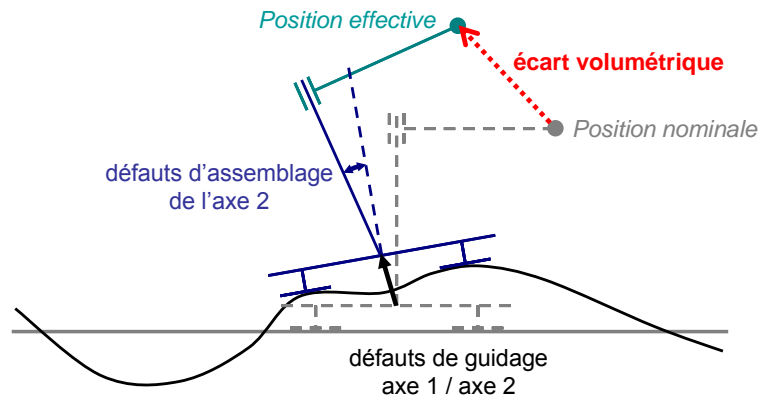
Erreurs géométriques (défauts de guidage et d'assemblage) – [EKINCI et al. 07]
